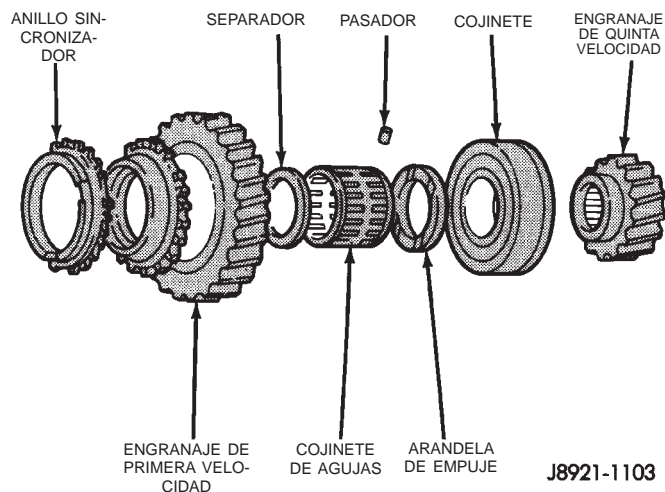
Componentes del engranaje de primera y quinta velocidad
